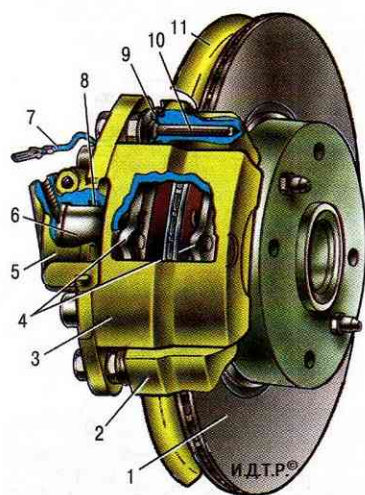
Тормозной механизм переднего колеса: 1 - тормозной диск; 2 - направляющая колодки; 3 - суппорт; 4 - тормозные колодки; 5 - цилиндр; 6 - поршень; 7 - сигнализатор износа колодок; 8 - уплотнительное кольцо; 9 - защитный чехол направляющего пальца; 10 - направляющий палец; 11 - защитный кожух
